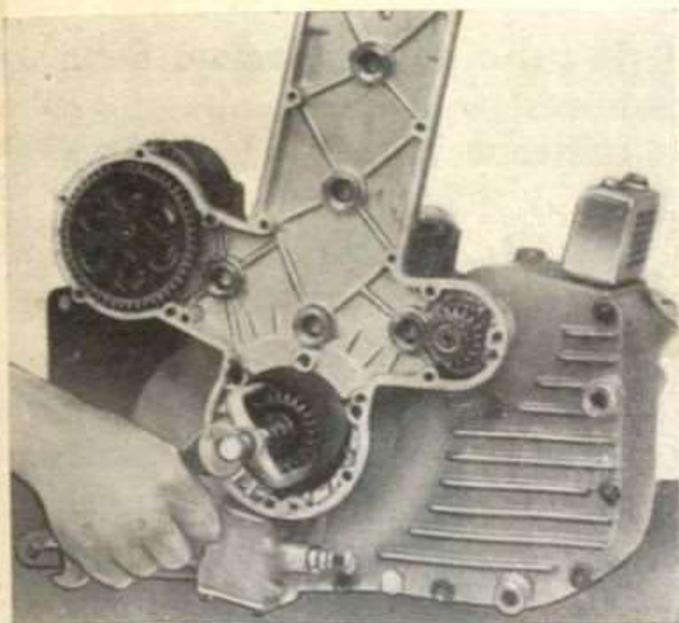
A 6-7 Estrattore ingranaggio motore lato distribuzione
